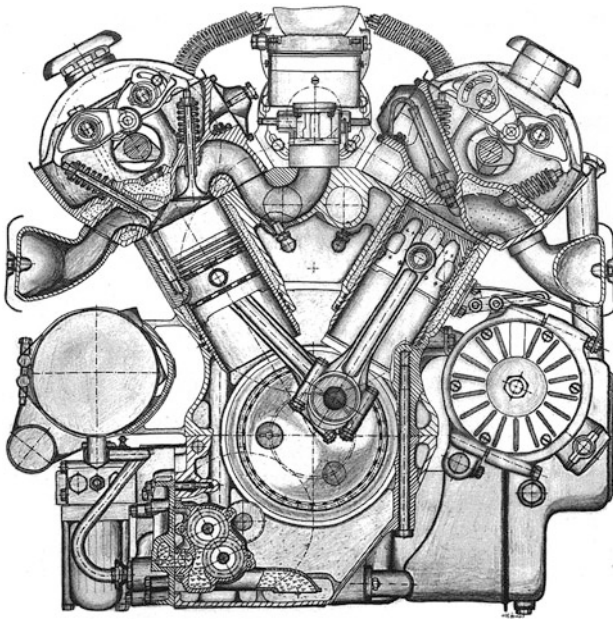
Der 220 kW (300 PS) starke Maybach-HL-120-Motor (hier: Querschnitt) war der Standardantrieb der Panzer III und IV: ein kompakter Zwölfzylinder-V-Motor, wobei das Motorzubehör geschickt am und im Motor integriert war
